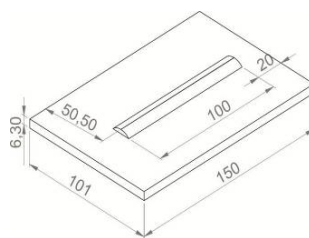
Dimensões, em milímetros, dos corpos de provas utilizados e dos cordões de solda.
